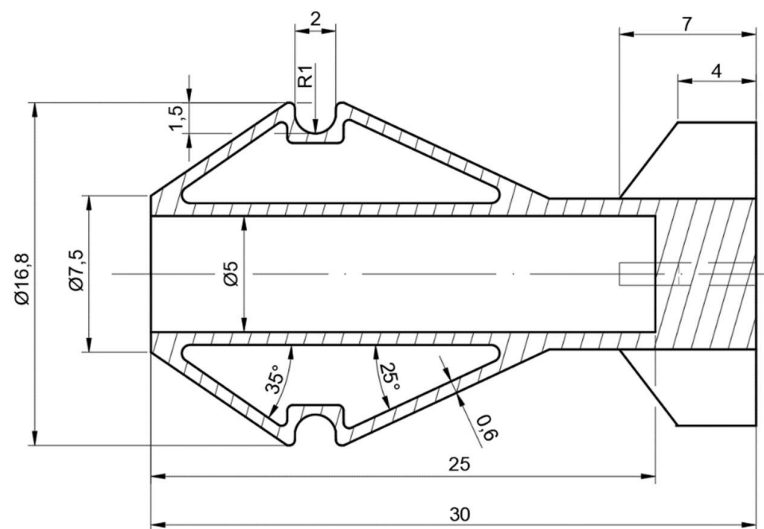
Princíp labyrintového tesnenia [37; 39]
